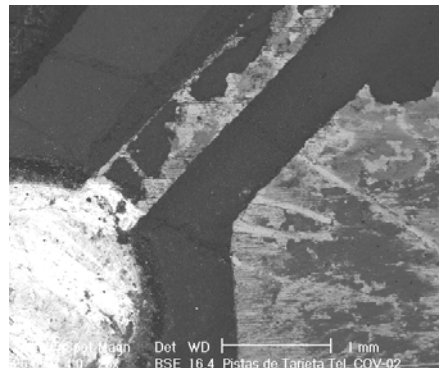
Detalle de una sección de la pista de la tarjeta impresa en una zona de soldadura. [Ortiz, A., 2003]
